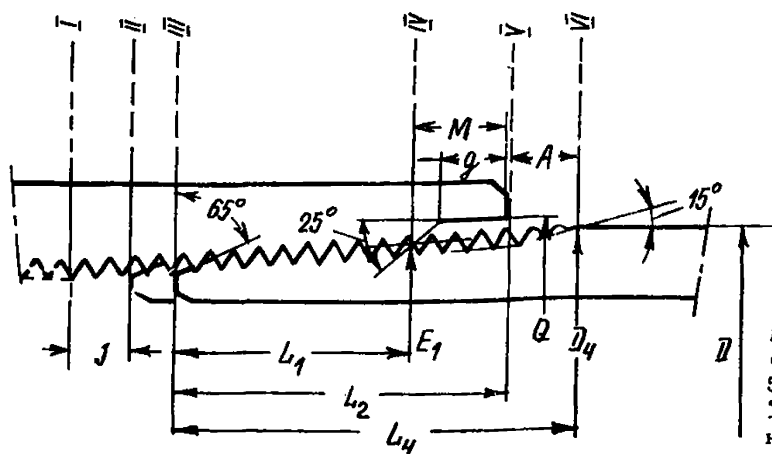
Резьбовое соединение насосно-компрессорных труб (по стандарту 5В АНИ). Плоскости: I - середины муфты или наименьшего диаметра резьбы муфтовой части;
